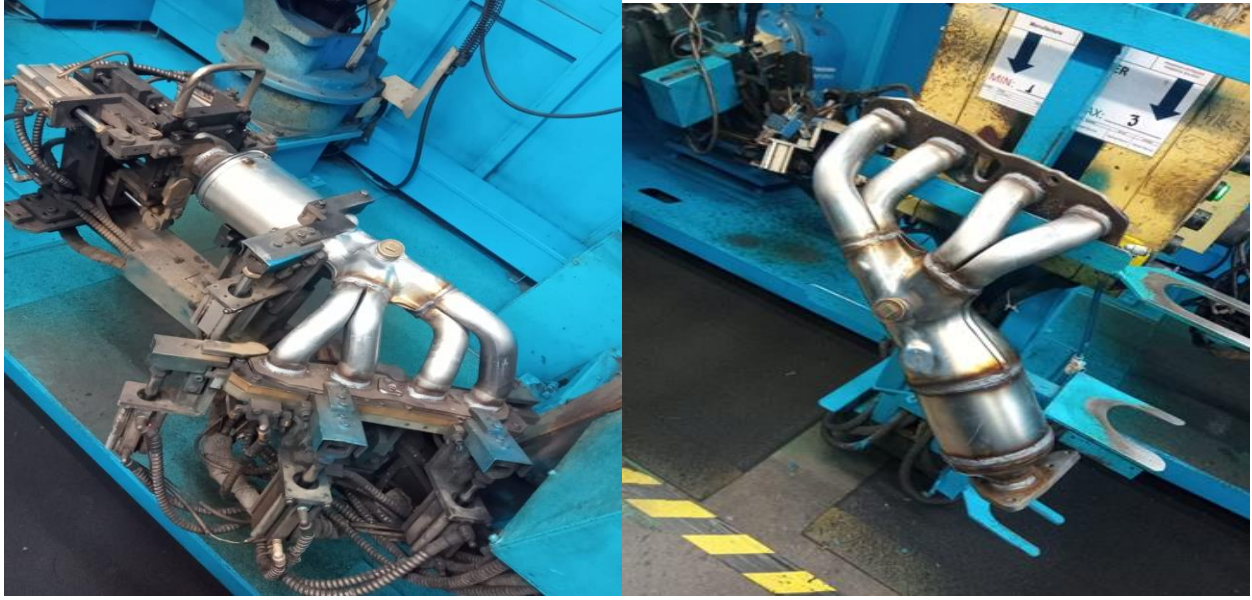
Imágenes referentes a la cabina #4 (lado A) de soldadura.
